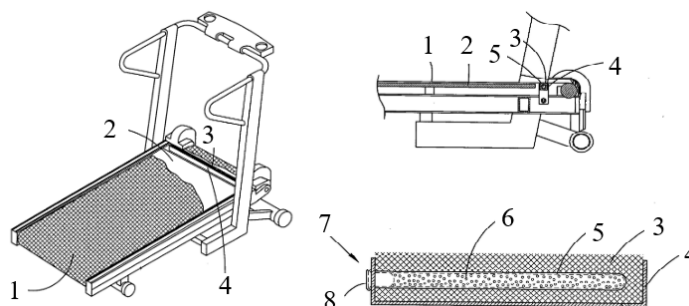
устройство смазочного аппарата для беговой дорожки
